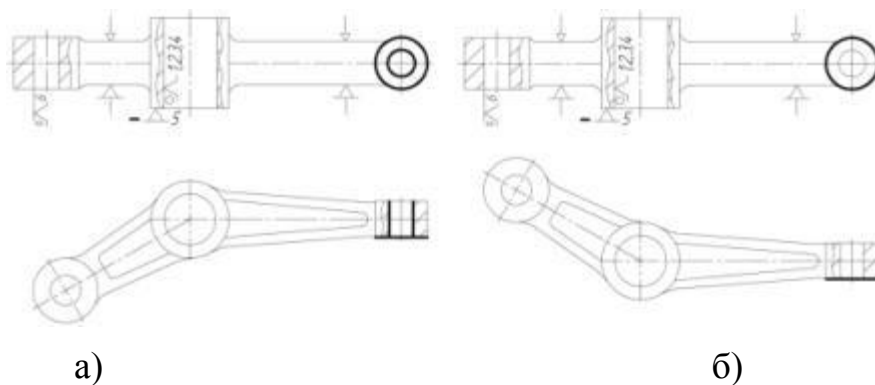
Схема базування заготовки на горизонтально-фрезерній 30 операції:
